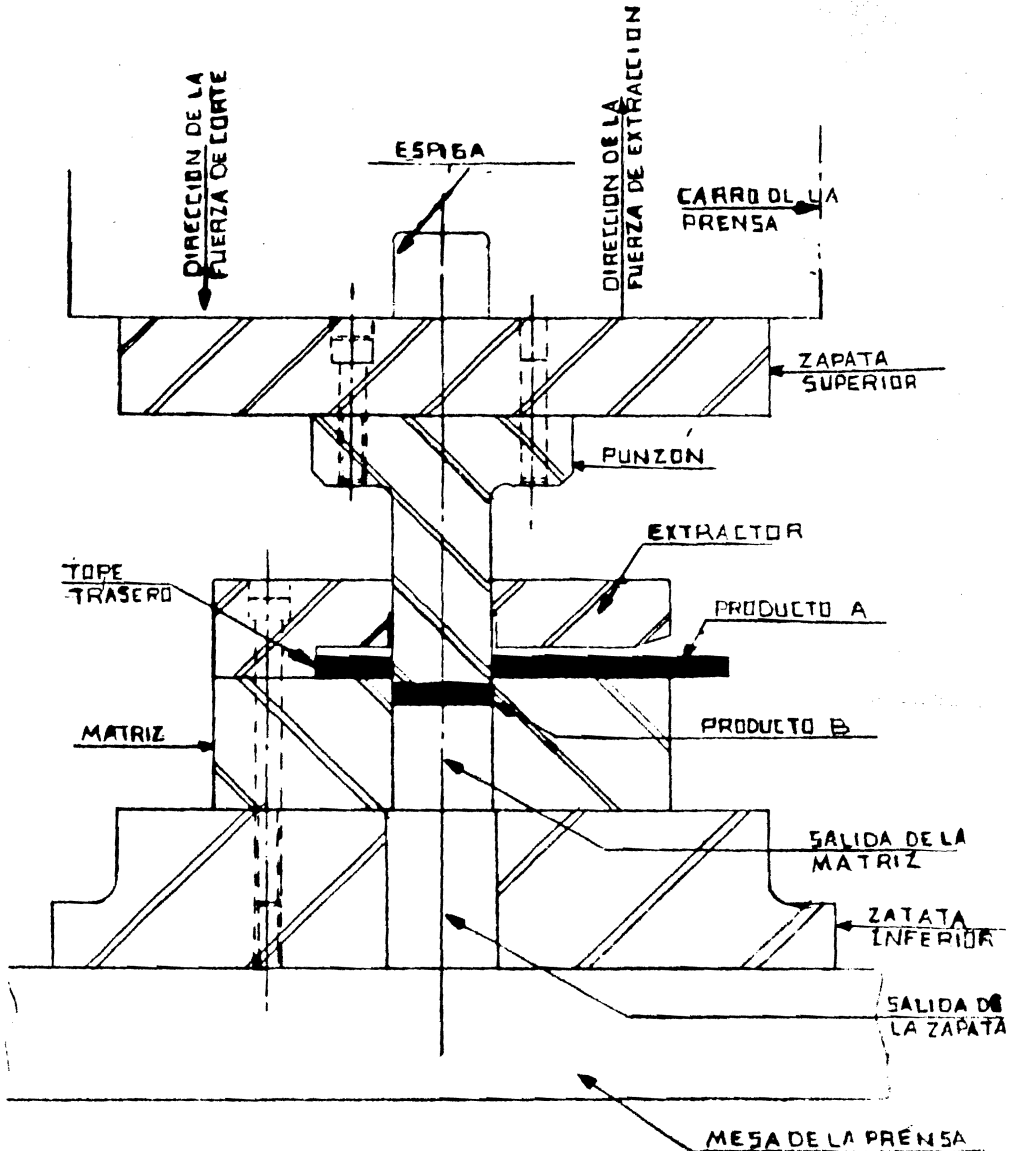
Designación de partes de un troquel simple de corte y/o punzonado.
